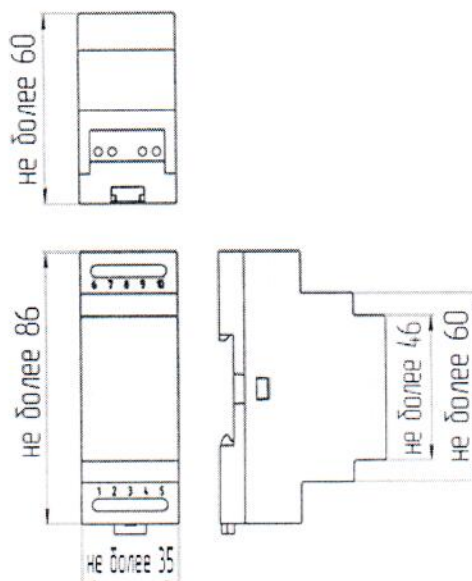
Преобразователь с HART протоколом в корпусе Д для крепления на DIN-рейку. Степень защиты оболочки IP20.
